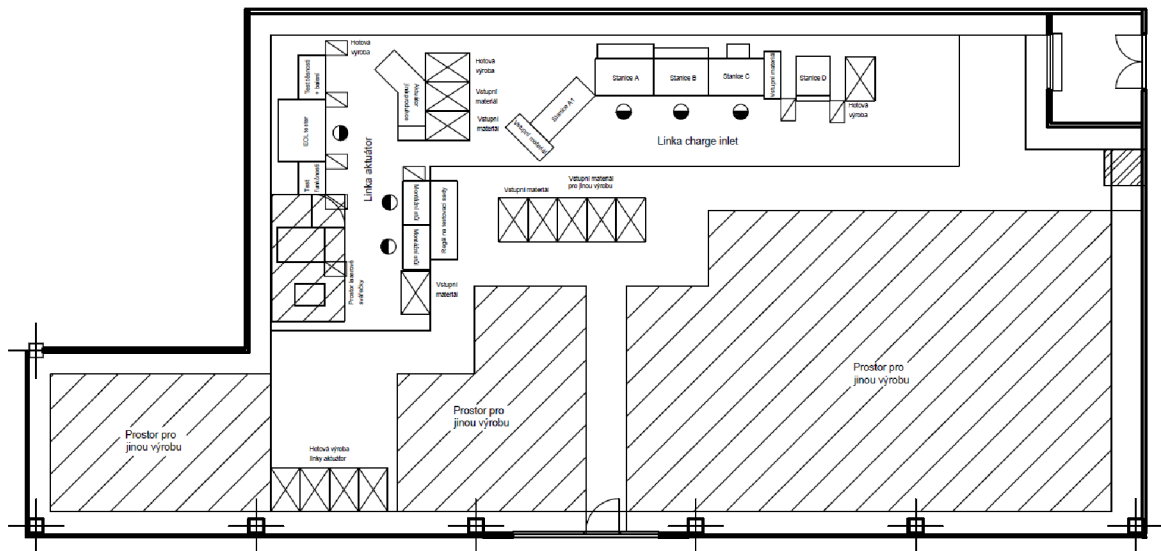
Detail současného layoutu výrobní linky charge inlet
